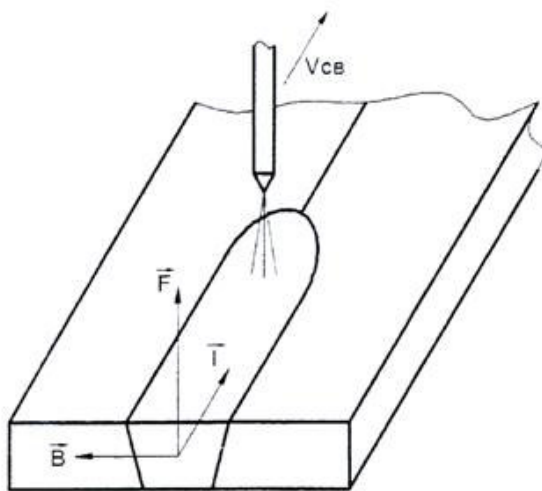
Схема удержания сварочной ванны поперечным магнитным полем
